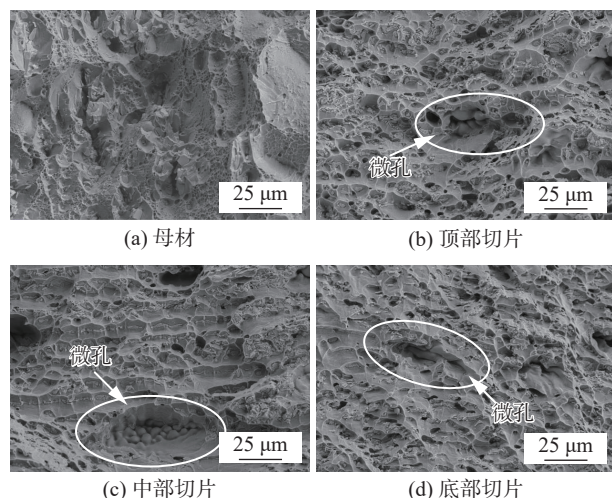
焊缝拉伸断口表面扫描电镜形貌
